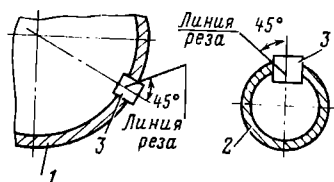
Вырезка патрубков из коллектора и «колокольчиков» из барабана:
